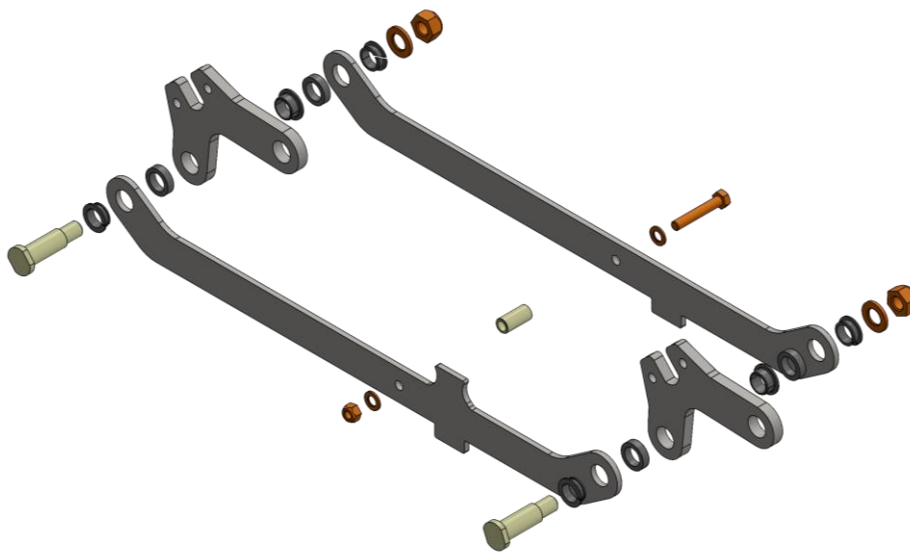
Ligação braço de elevação e barras de sincronismo, vista explodida
